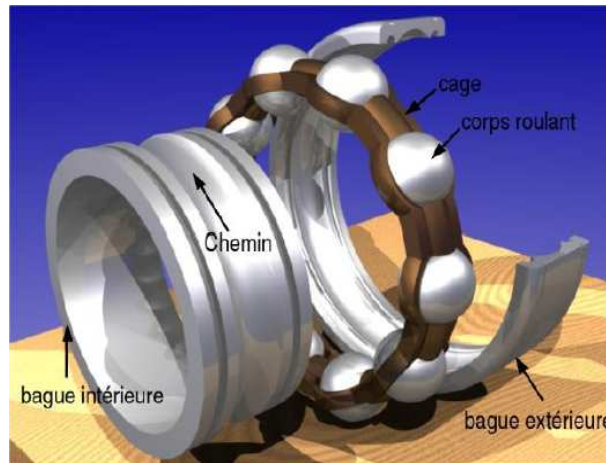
Vue éclatée d'un roulement à billes [14].
